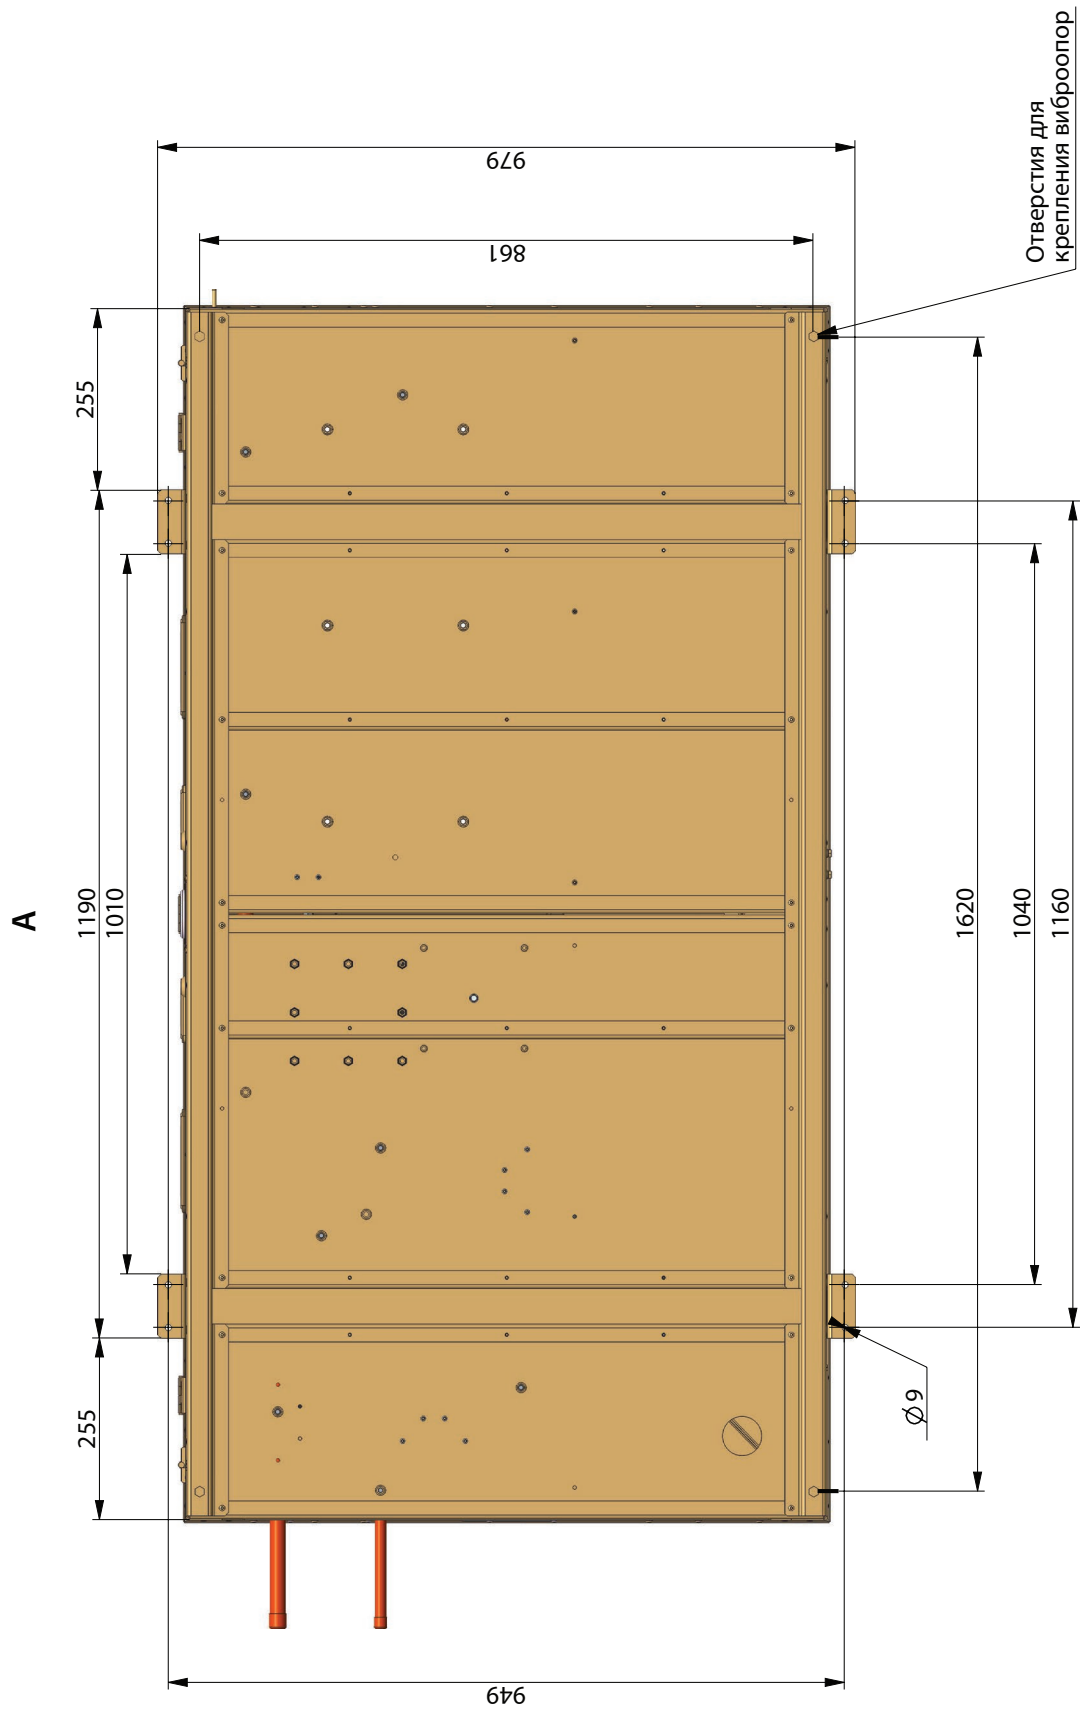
Агрегат компрессорный типа МАКК 320-301, -351
